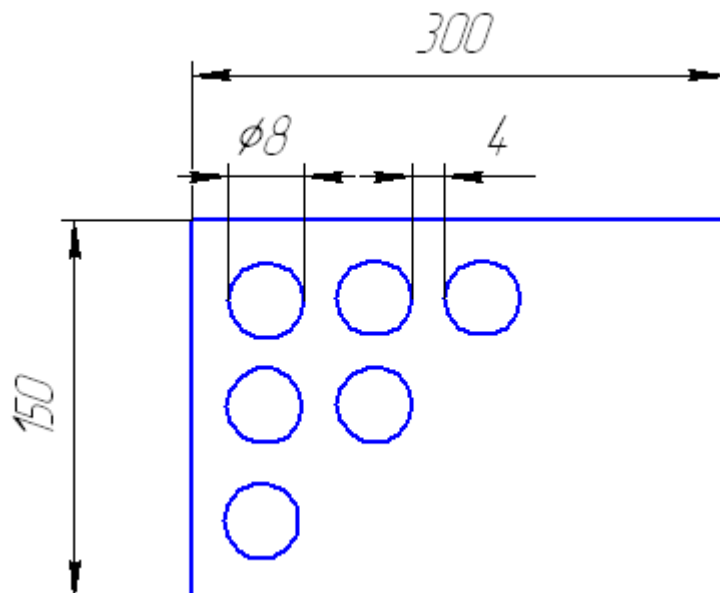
Схема садки печі СВС – 1,5.3.4/8,5
